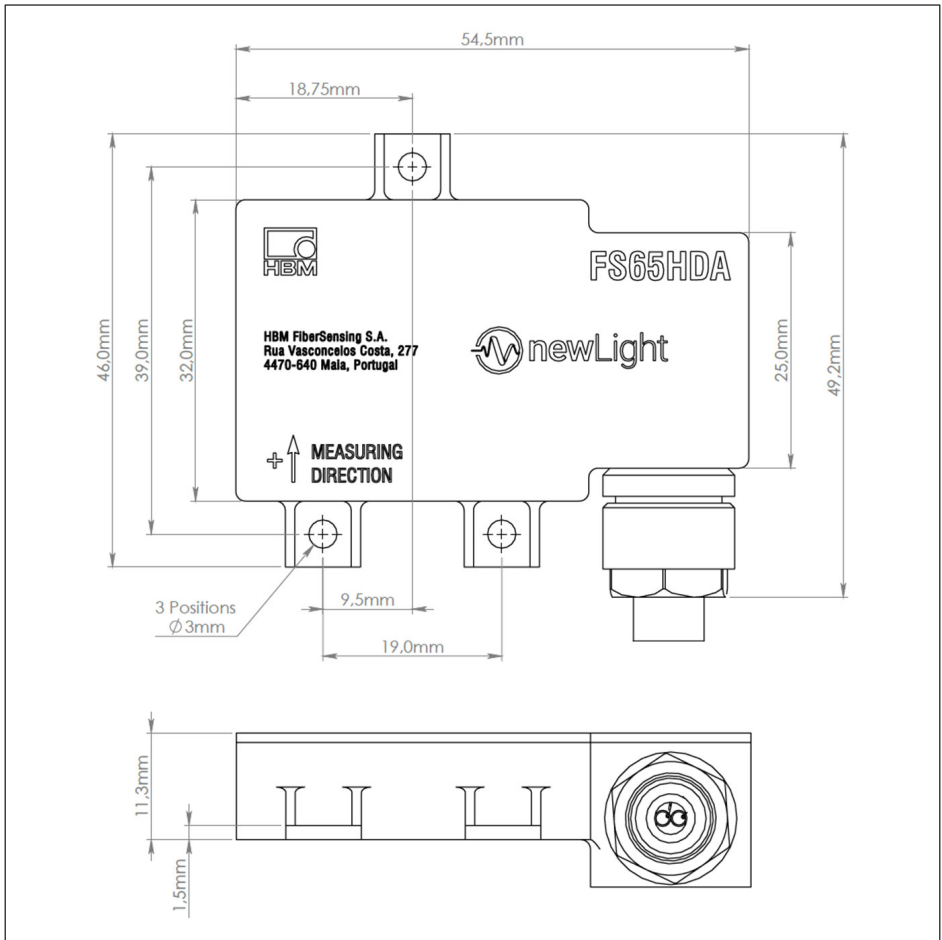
Technische Zeichnung des Beschleunigungssensors für hohe Beanspruchung FS65HDA (Abmessungen in mm)
